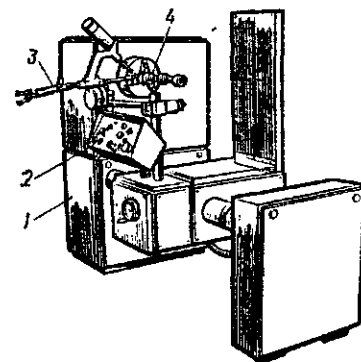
Установка О11-1-09 ВНПО «Ремдеталь» для газопламенного напыления порошковых материалов на детали типа тел вращения:
